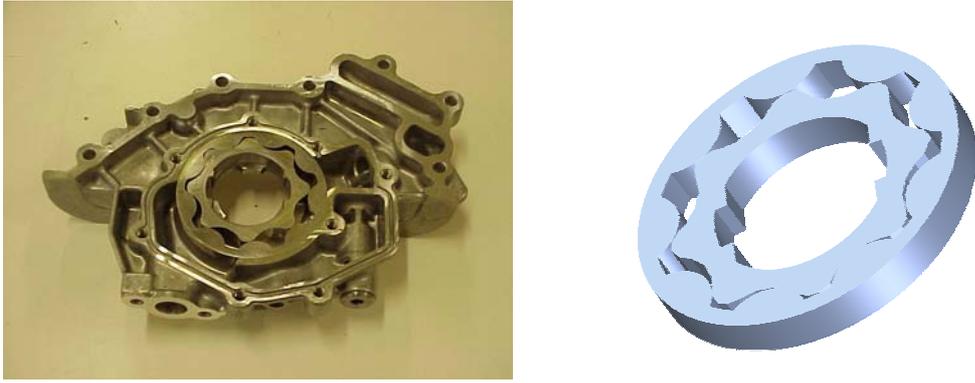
Bomba gerotor de lubricación de un motor de combustión interna (izquierda) y conjunto rueda dentada interior y exterior generadas por perfiles trocoidales (derecha)
